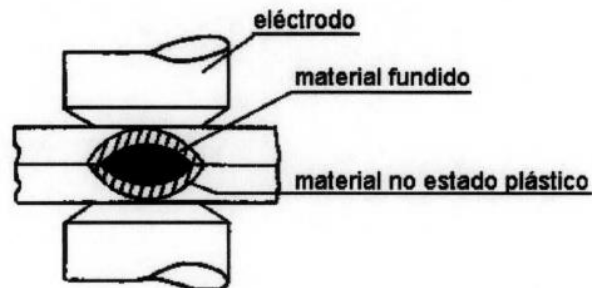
Formação de um Ponto de Soldadura na Zona de Contacto entre Peças [31].
